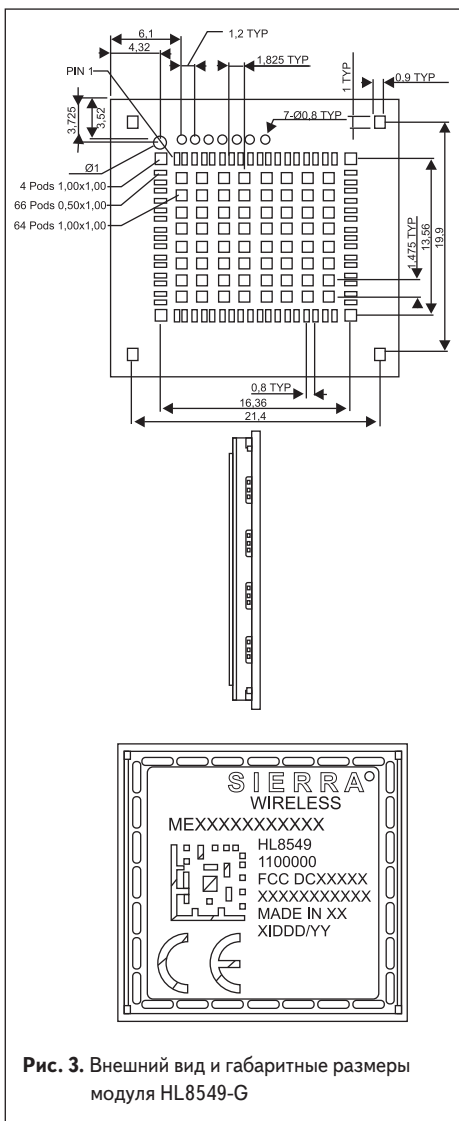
Внешний вид и габаритные размеры модуля HL8549-G
